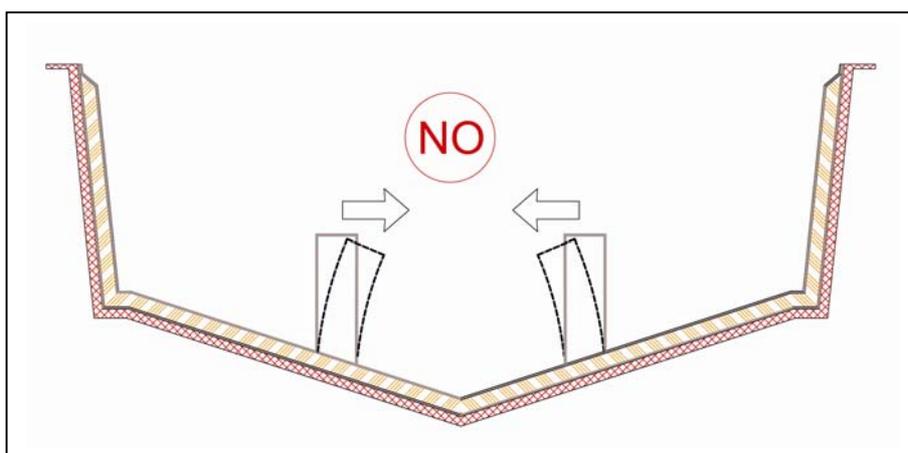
STRUTTURE DEFORMATE DALL'AZIONE DEL "VUOTO"
